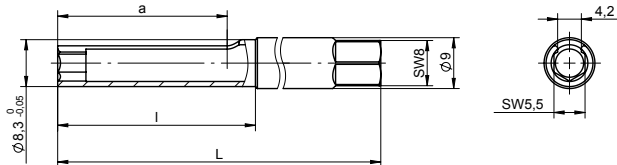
Montagewerkzeug Typ 1300B12 (a 40, l 45, L 100),
